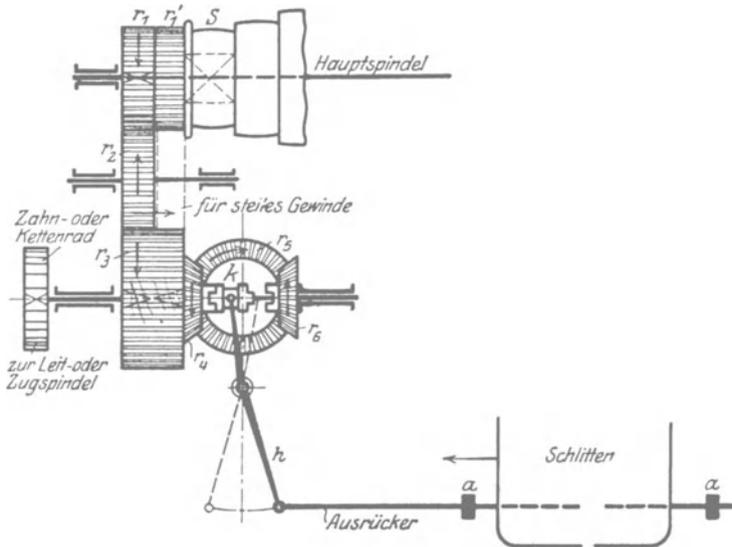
Kegelräderwendegetriebe mit Selbstausrücker.
